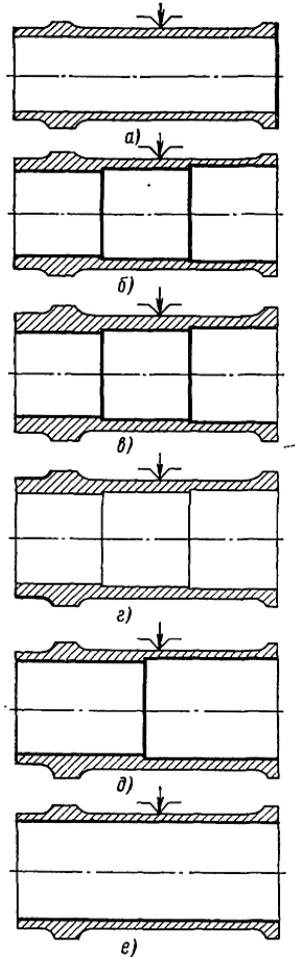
Схема обработки заготовок на многопозиционном агрегатном станке:
